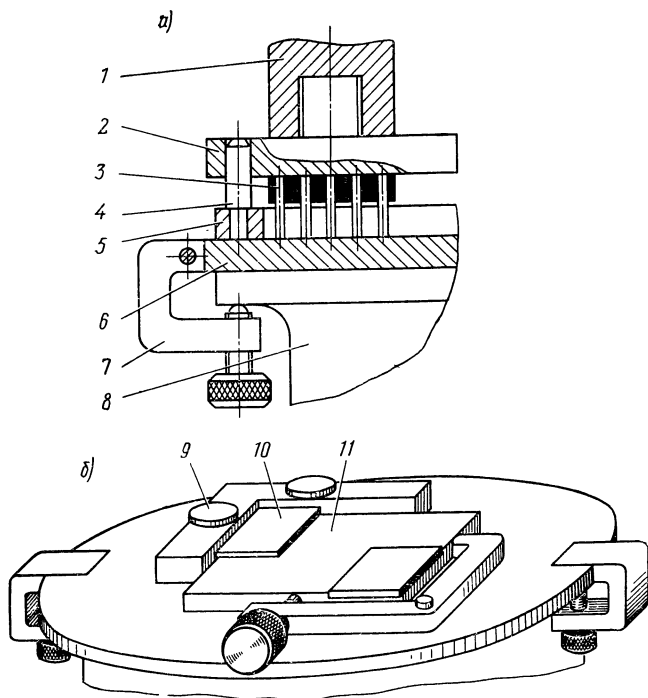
Схема ориентирования приспособления для крепления заготовок по инструменту (а) и заготовки в приспособлении (б):
